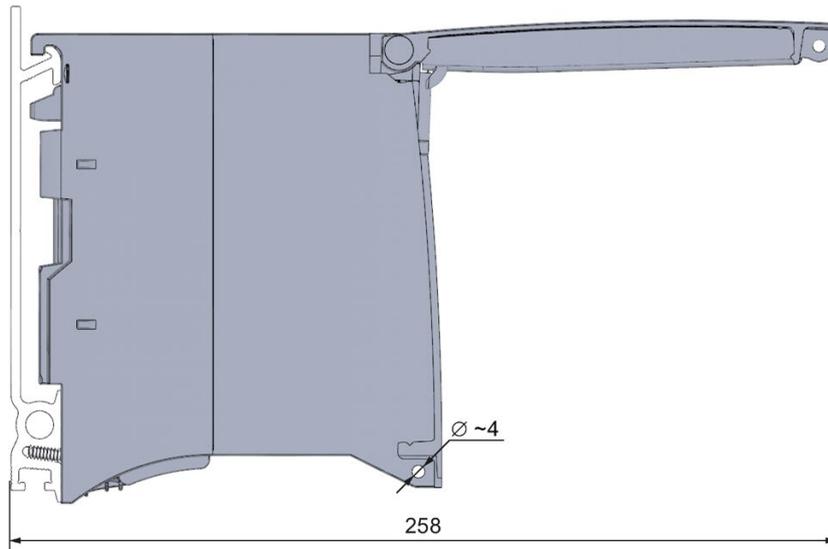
Maßbild CPU 1518-4 PN/DP MFP, Seitenansicht mit geöffneter Frontklappe
